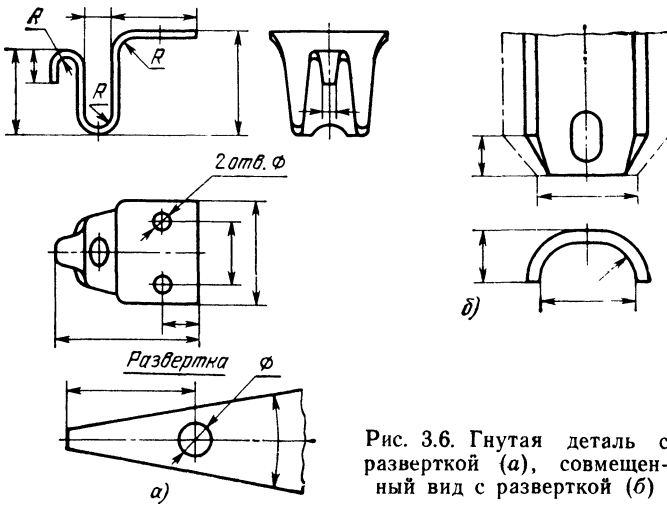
Гнутая деталь с разверткой (а), совмещенный вид с разверткой (б)
